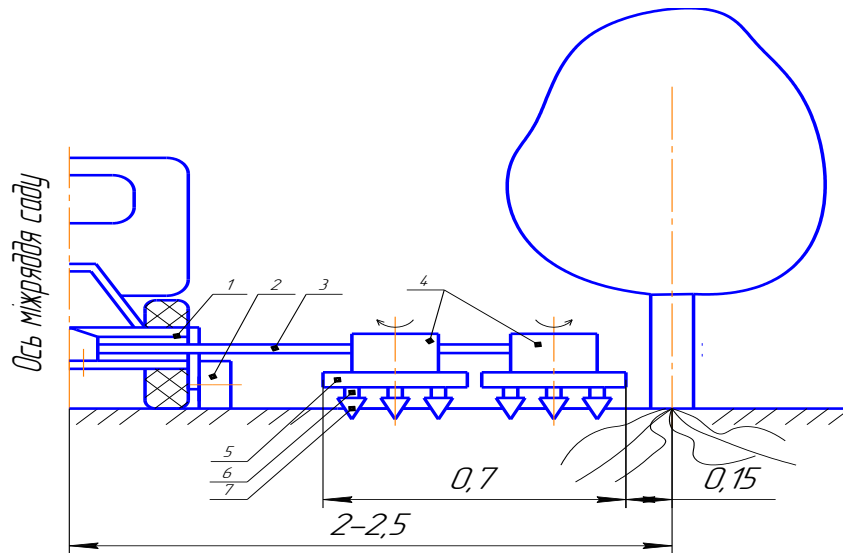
Конструктивно – технологічна схема фрезерної машини:
